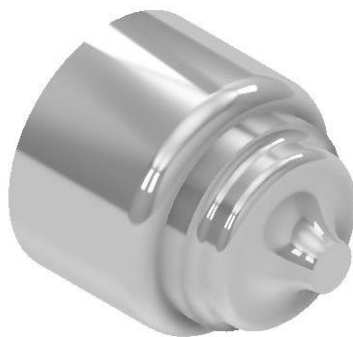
Τρισδιάστατη απεικόνιση αποστολής 39
